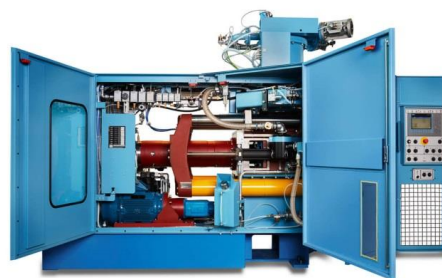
Detalle de los cilindros que realizan la presión de moldeo.
